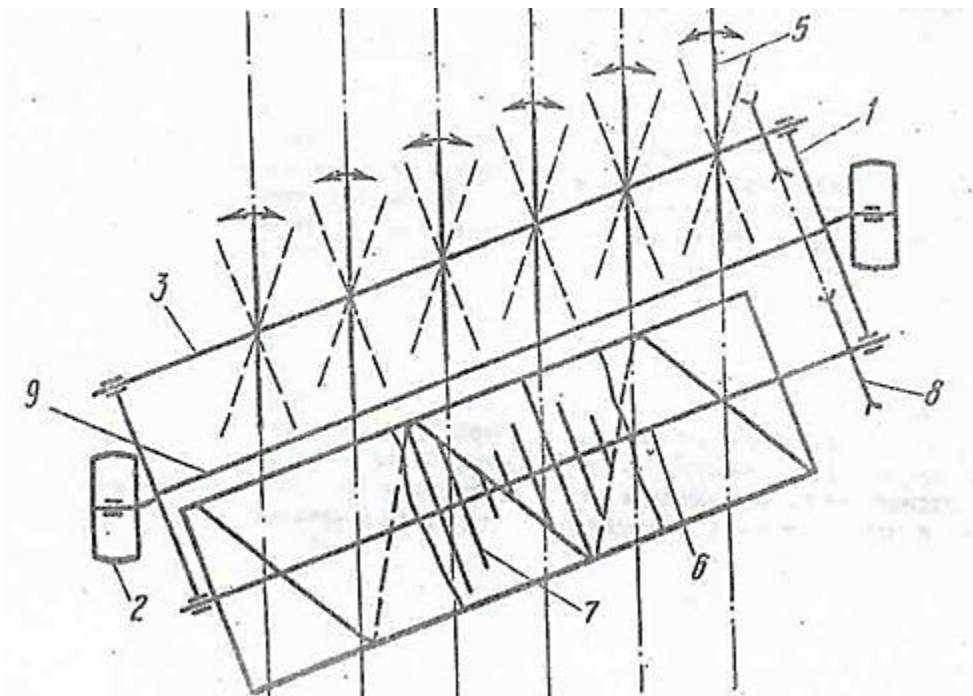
Схема очисника головок коренеплодів [9], вид зверху
